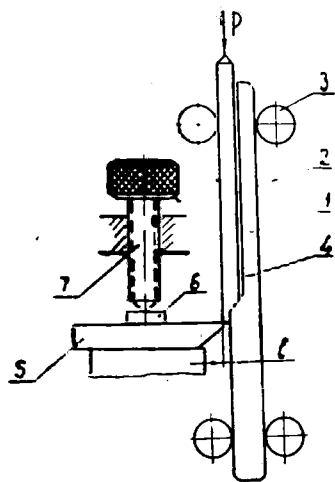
Принципиальная схема приспособления для микроиспытания резцов.
